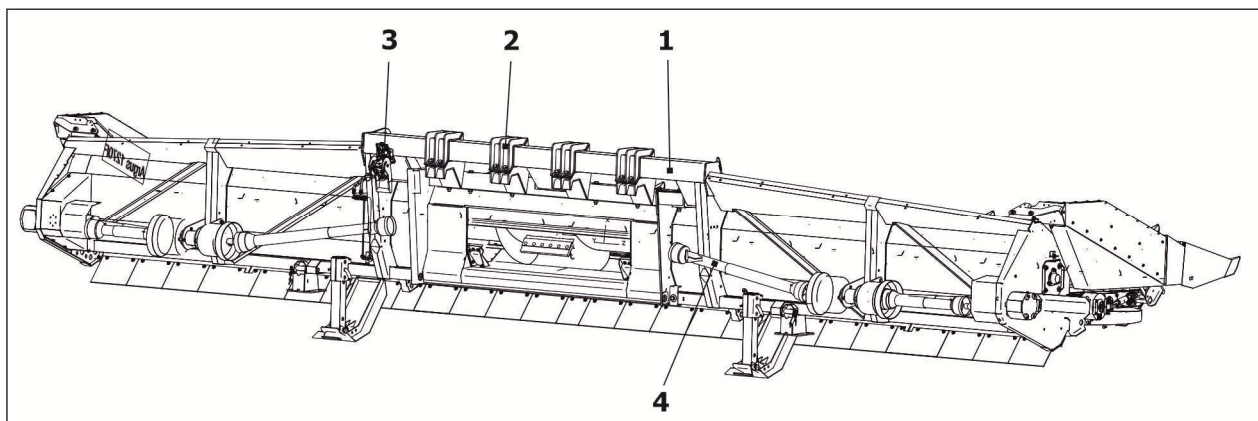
Гидравлическая регулировка отрывных пластин русла
